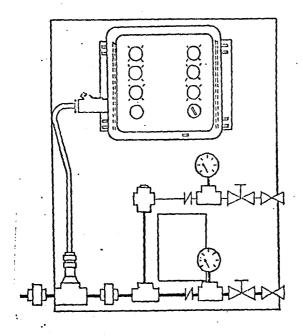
TABLERO TIPICO CON PILOTO & INDICADOR
